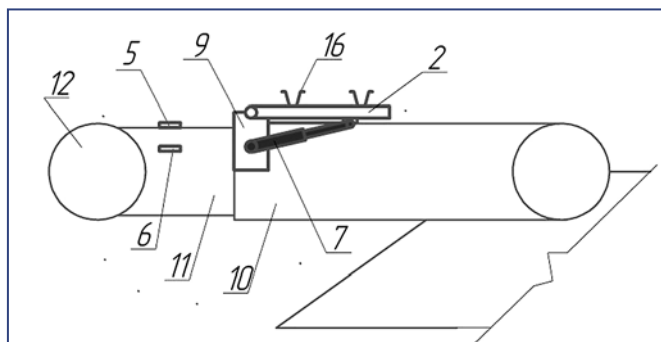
Исполнительный орган комбайна с крепеподъемником (вид сбоку)
